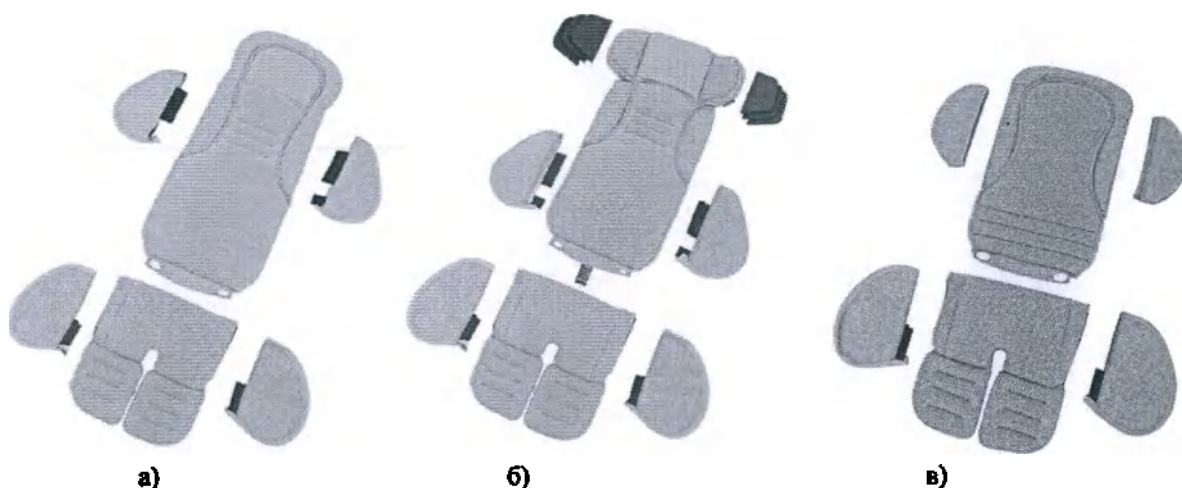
А. Обшивка для спинки: а) стандартной; б) со встроенным подголовником; в) короткой.
